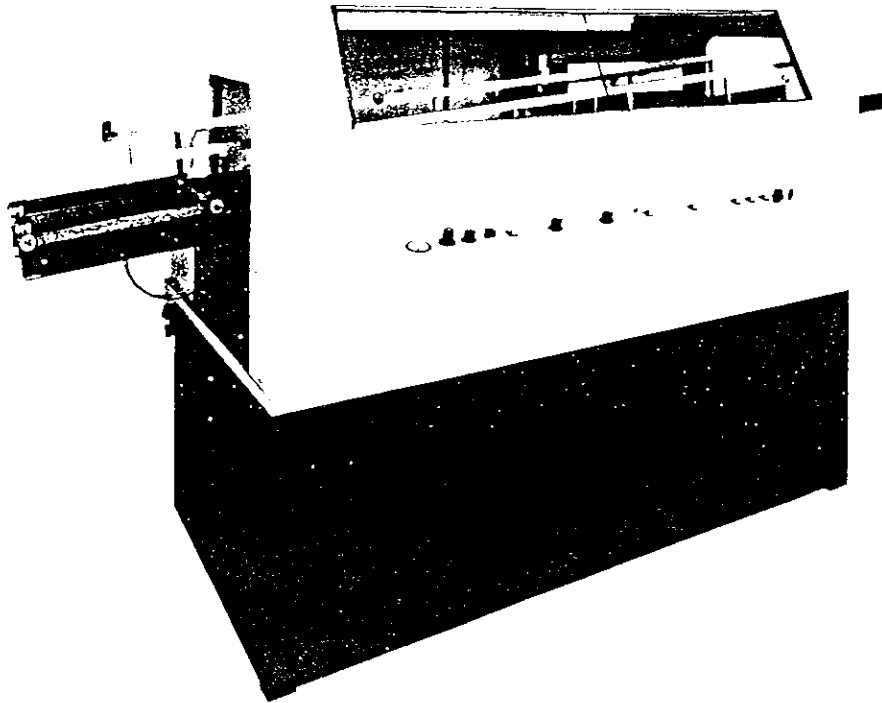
A SISTEMAS AUTOMATICOS DE SOLDADURA
